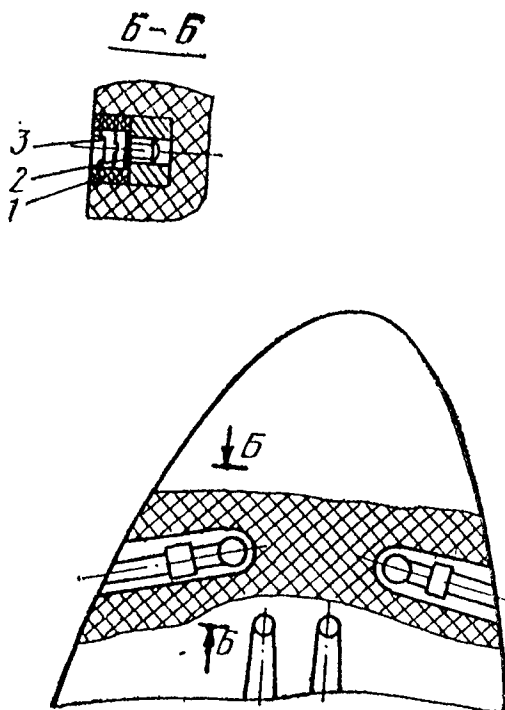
К замене нагревательной накладки воздушного винта:
